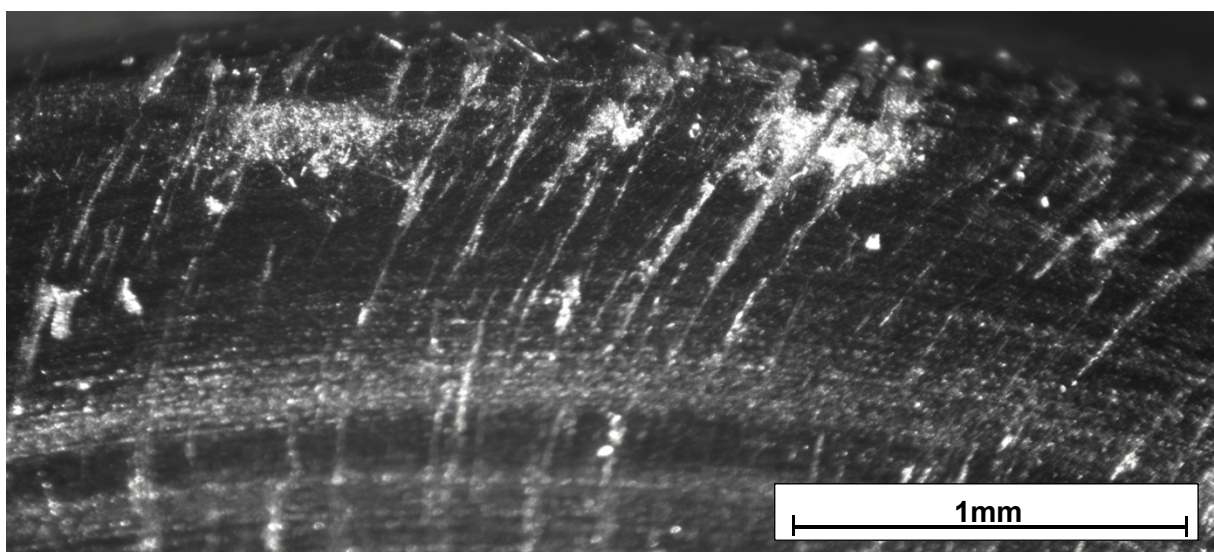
Gleitfläche der Trapezgewindespindel des Zustands „+C“ mit Sichelform
